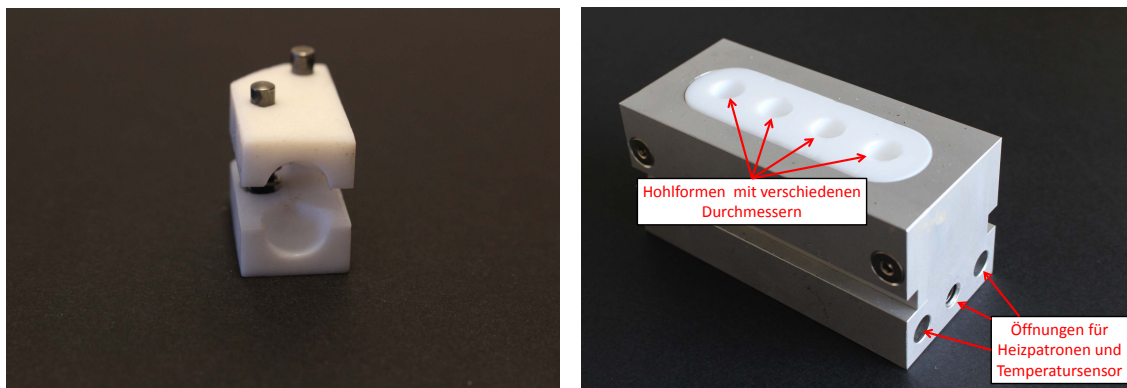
Formteile zum Verschließen der Hohlzylinder. PTFE-Hohlform (links), beheizbarer Aluminiumblock mit PTFE-Formteil (rechts)
